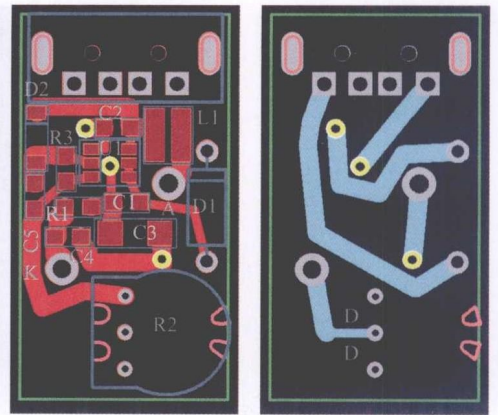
USB 灯 PCB 顶视图和 X 光底视图
